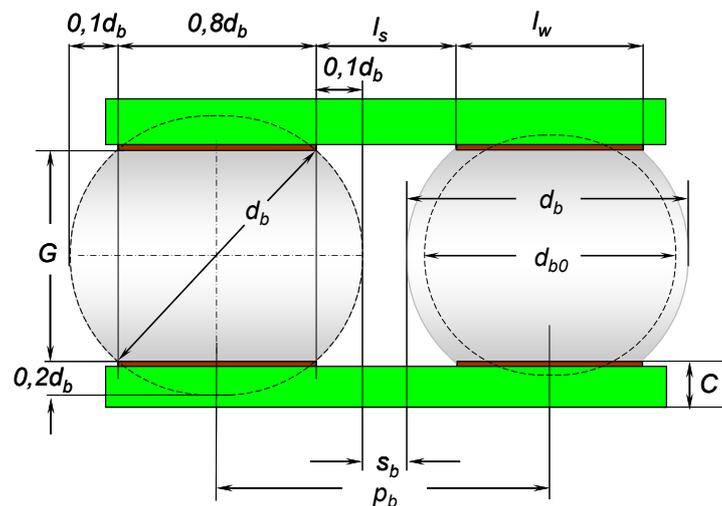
Notwendige Daten für die Berechnung der Geometrie von Solder Bump
